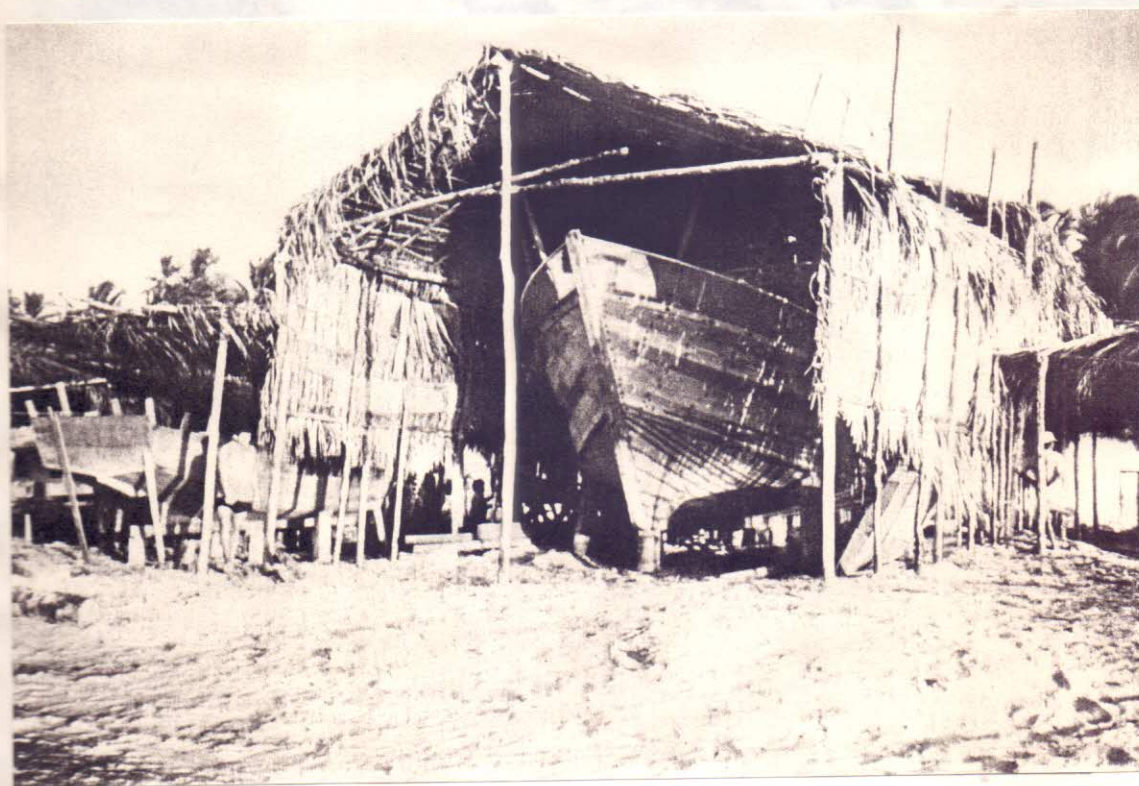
Barco lagosteiro em construção em um estaleiro improvisado na praia.
